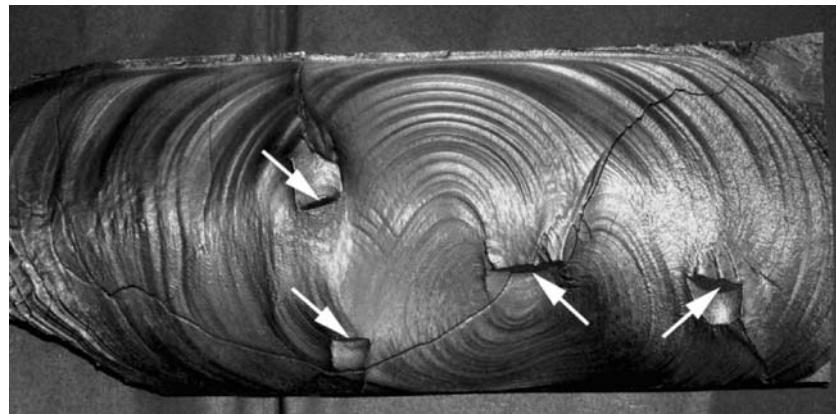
Вид поверхности усталостного разрушения бракованного колеса. Очагами разрушения послужили флокены (показаны стрелками).
